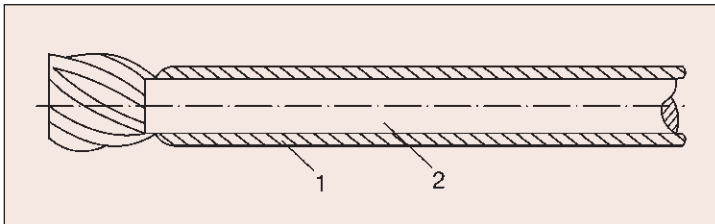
Соединение многожильного провода 1 с проволокой 2
